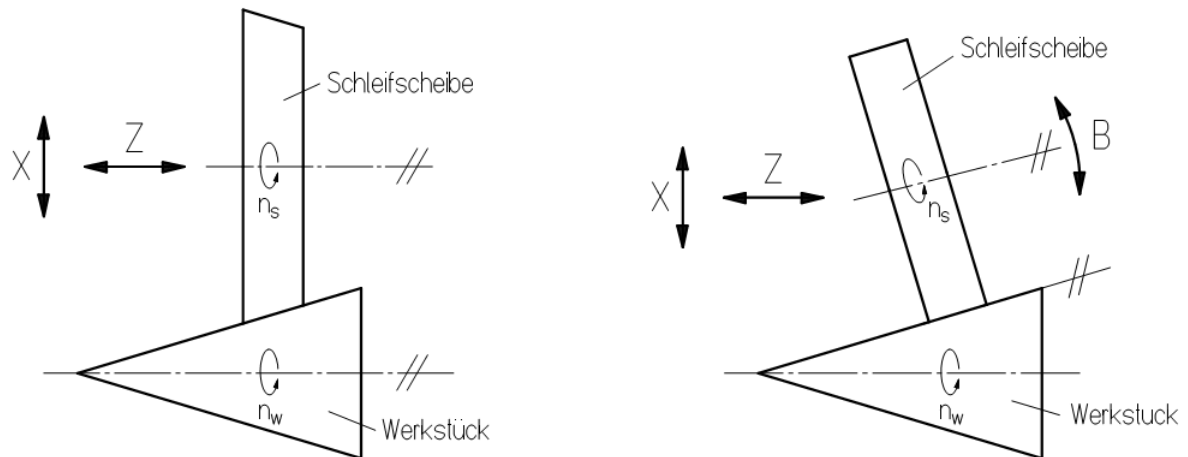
Kegelschleifen mit einer kegelig abgerichteten (links) und einer um die B-Achse geschwenkten zylindrischen Schleifscheibe (rechts)
